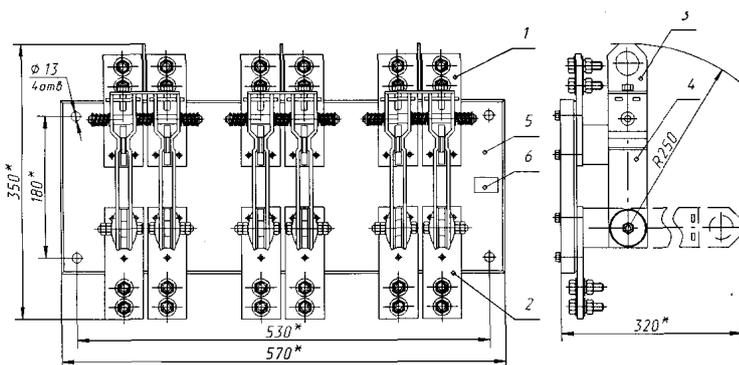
Общий вид, габаритные, установочные и присоединительные размеры рубильника РП-5-1000 УЗ:
